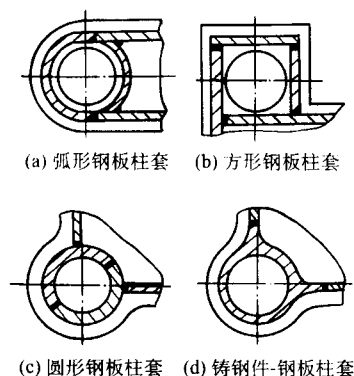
液压机横梁柱套的电弧焊接结构
